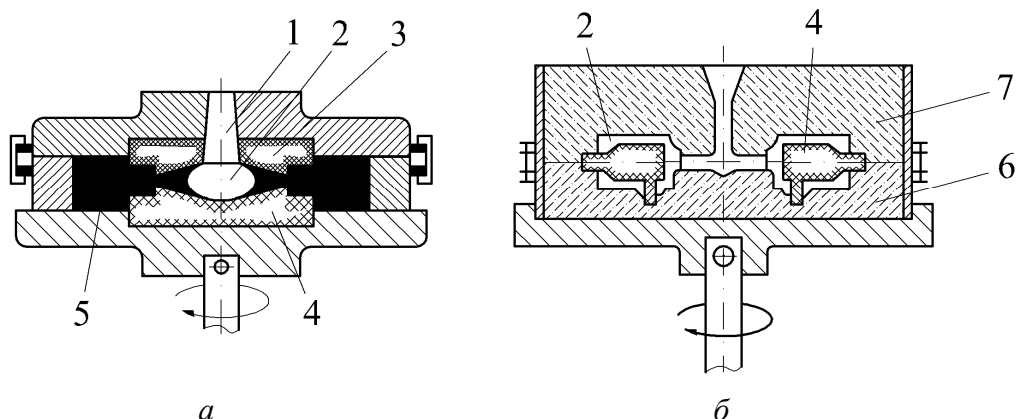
Схема получения фасонных отливок: а – венцов шестерен; б – мелких фасонных отливок; 1 – стояк; 2 – рабочая полость; 3, 4 – стержни; 5 – избыток расплава (сверх массы отливки); 6 – нижняя полуформа; 7 – верхняя полуформа
